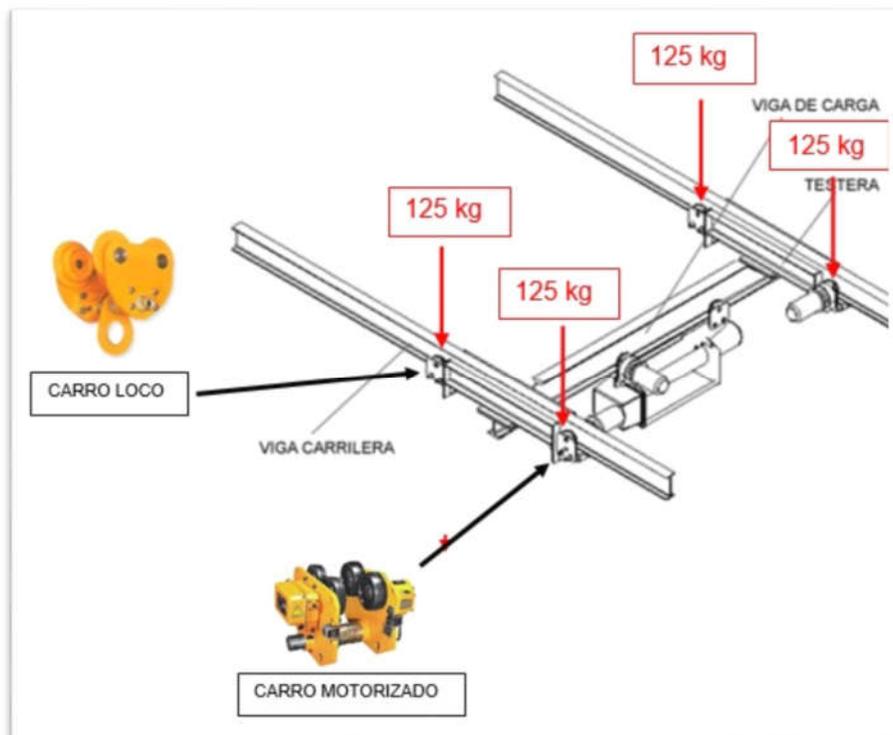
Cargas aplicadas sobre la viga carrilera
